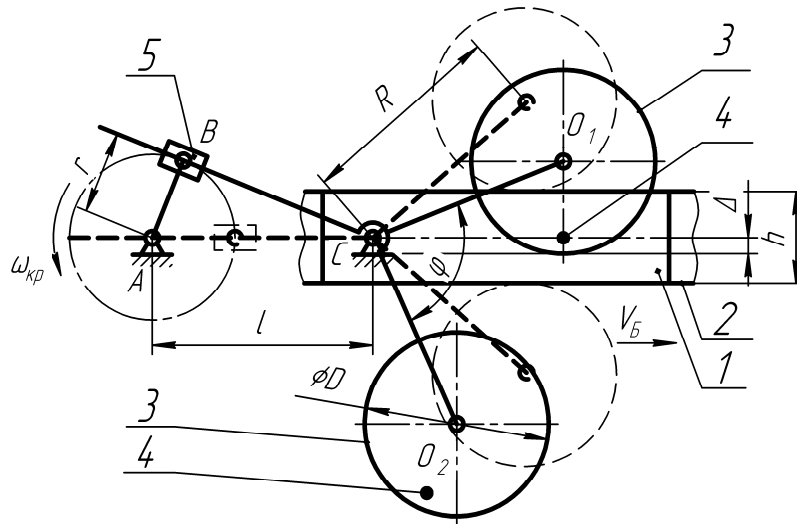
Схема пристрою для підготовки корінця до нанесення клею
